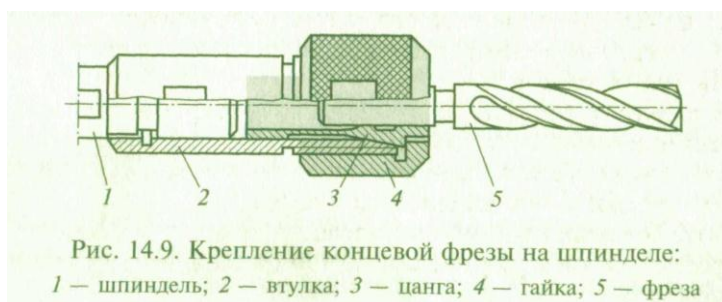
Крепление концевой фрезы на шпинделе:
